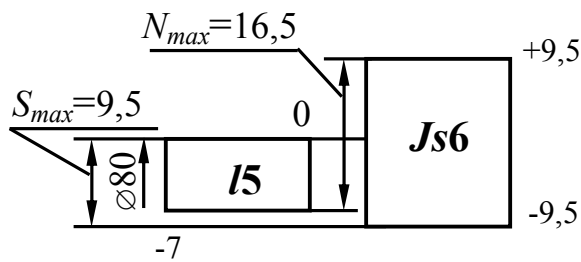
Схема розташування полів допусків для посадки зовнішнього кільця підшипника в корпус
